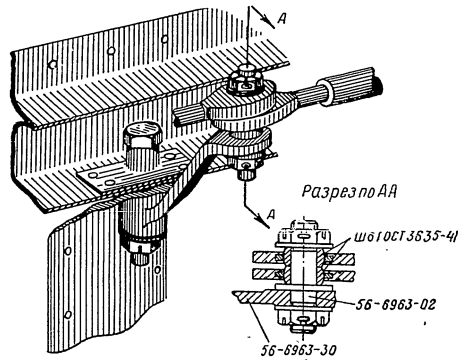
Узел крепления выхлопного коллектора двигателя.
